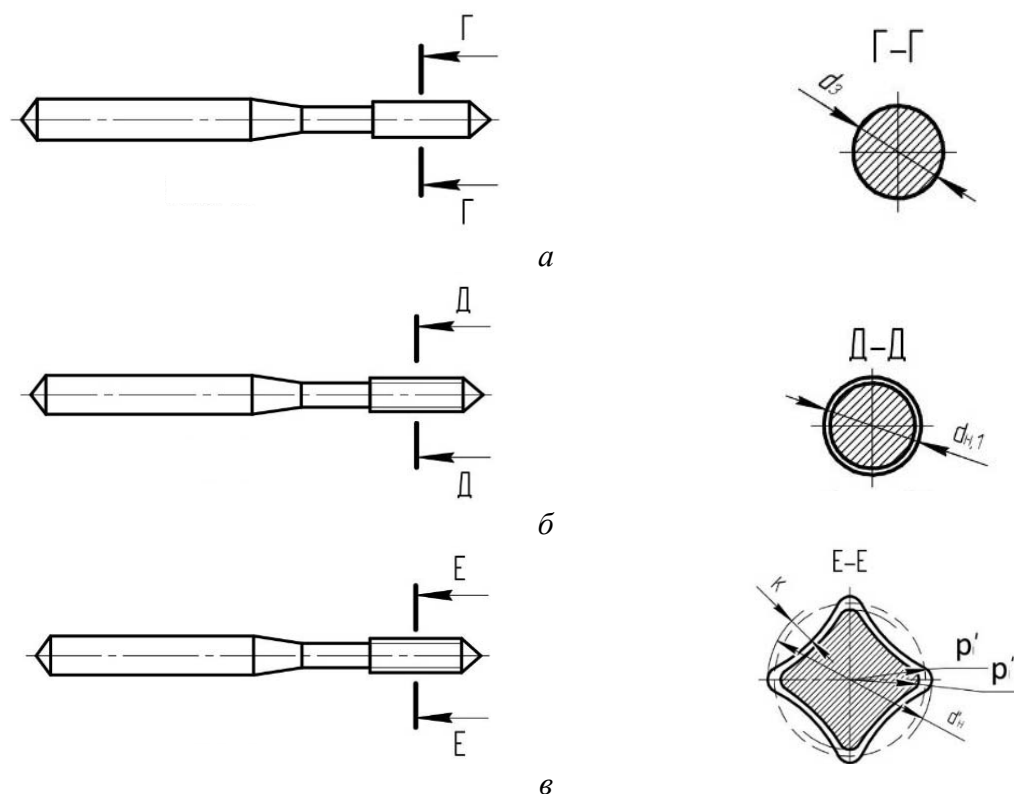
Схема способа формирования рабочей части ПДМ с полным профилем резьбы по всему сечению: а – заготовка ПДМ с рабочей частью круглого поперечного сечения Г-Г; б – заготовка с полным профилем резьбы по всему сечению Д-Д рабочей части; в – ПДМ с окончательно сформированным поперечным сечением Е-Е
